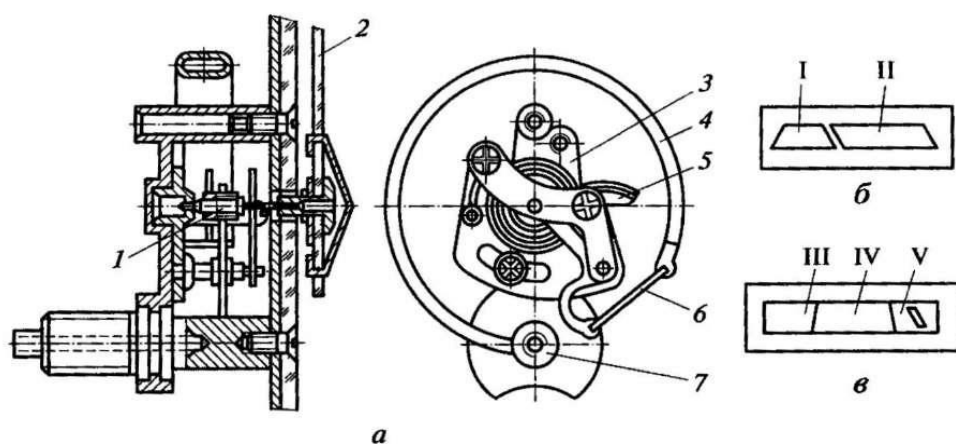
Указатель давления или разряжения с трубчатой пружиной: а — продольный разрез и вид сзади; б и в — шкалы эконометров; 1 — центрирующий узел; 2 — стрелка указателя; 3 — возвратная пружина; 4 — трубчатая пружина; 5 — зубчатый сектор; 6 — тяга; 7 — штуцер подвода воздуха; I — зона увеличенного расхода топлива; II — зона экономного расхода топлива; III — зона повышенного расхода топлива; IV — зона нормального расхода топлива; V — зона повышенного расхода топлива
